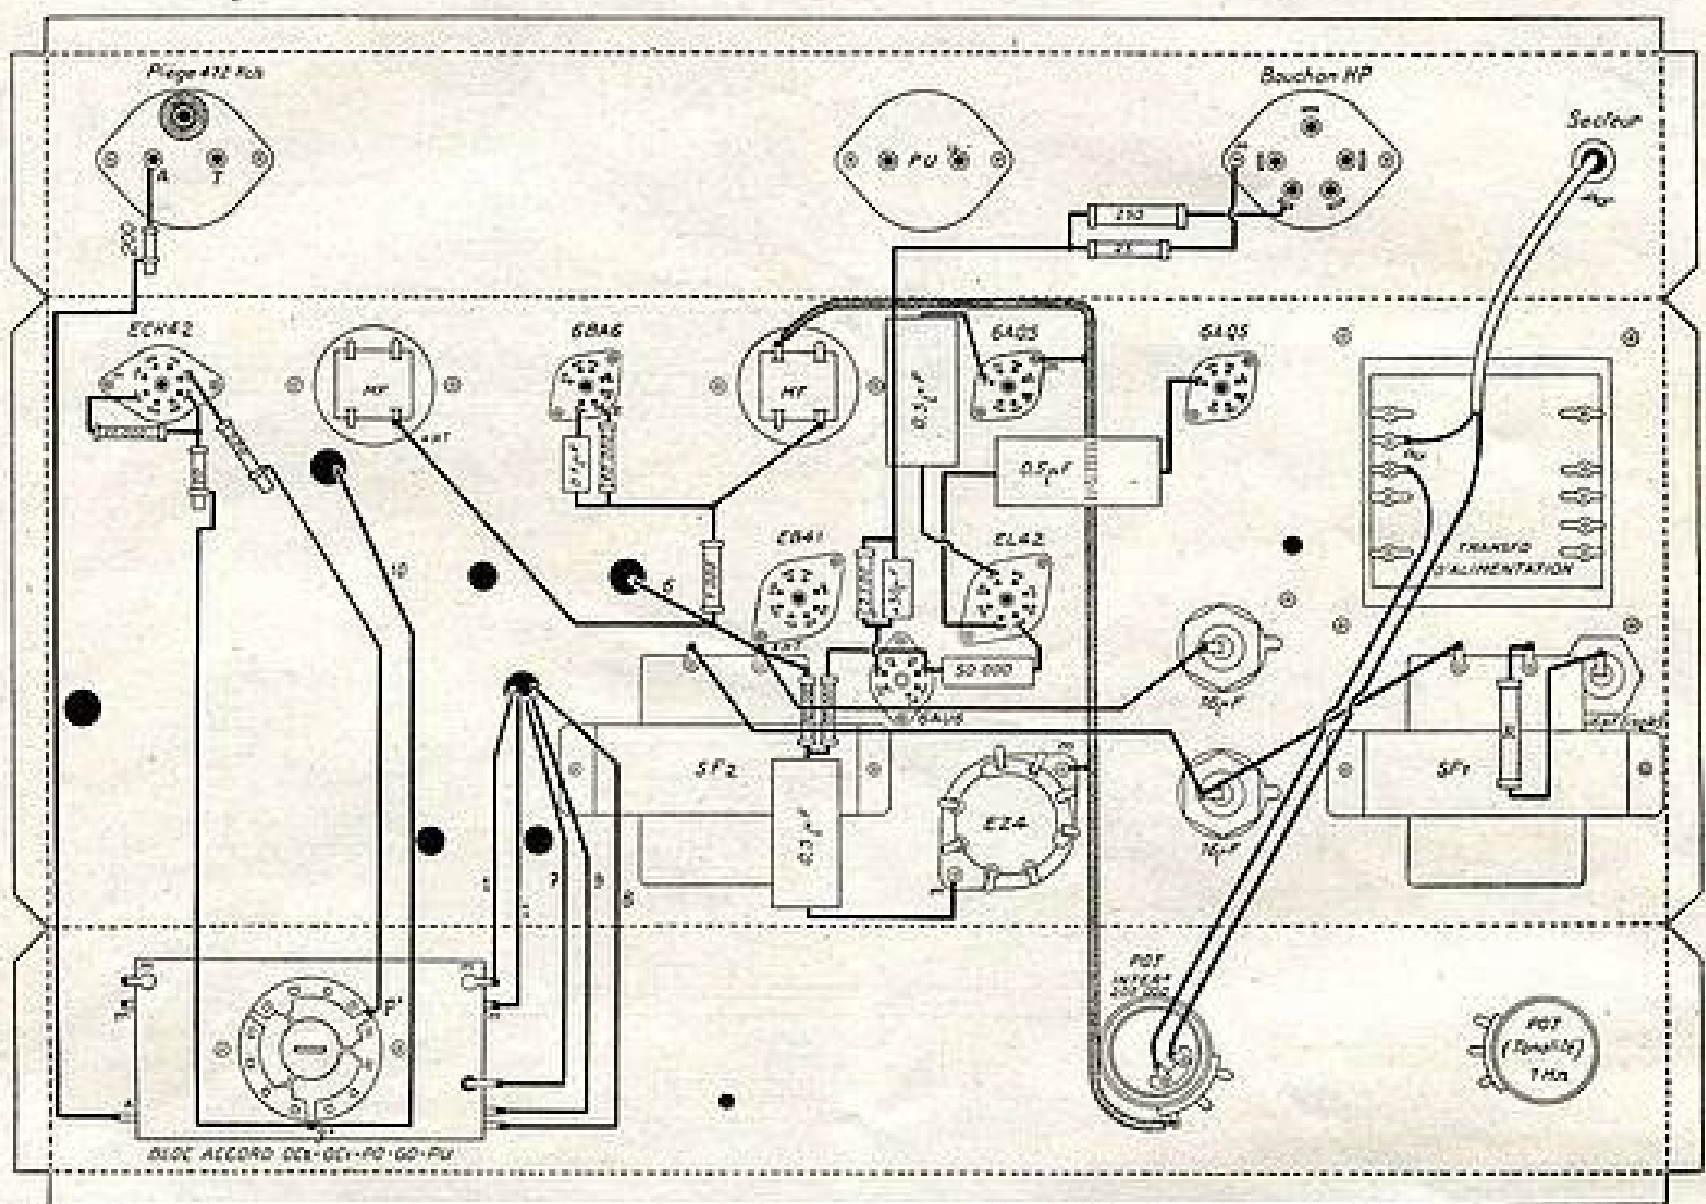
Plan D : câblage deuxième stade, sous le châssis.
